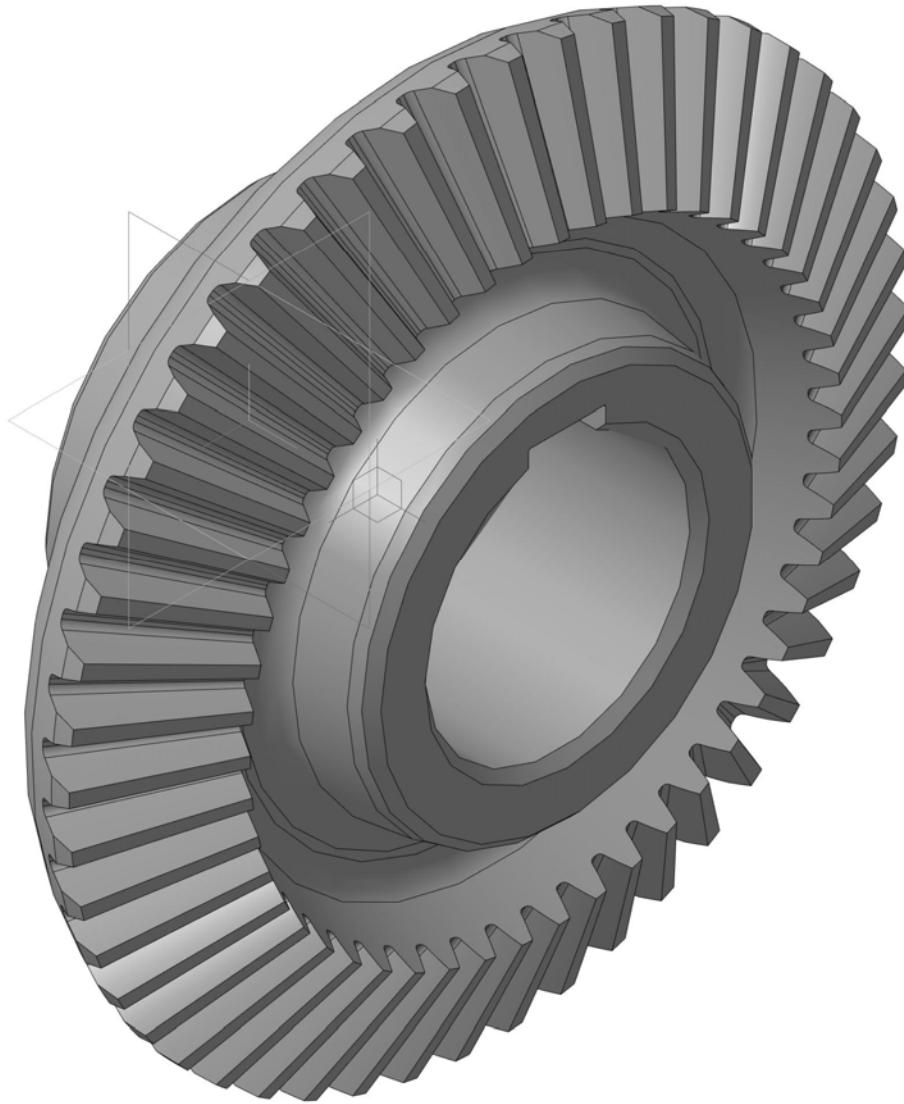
Cad-модель конічного зубчастого колеса
